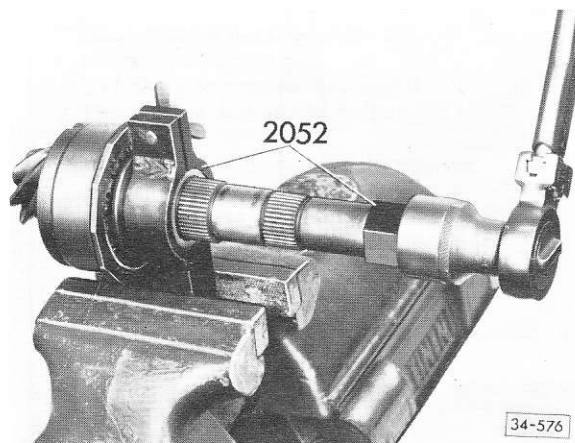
Bague intérieure/roulement à aiguilles: desserrage et serrage
